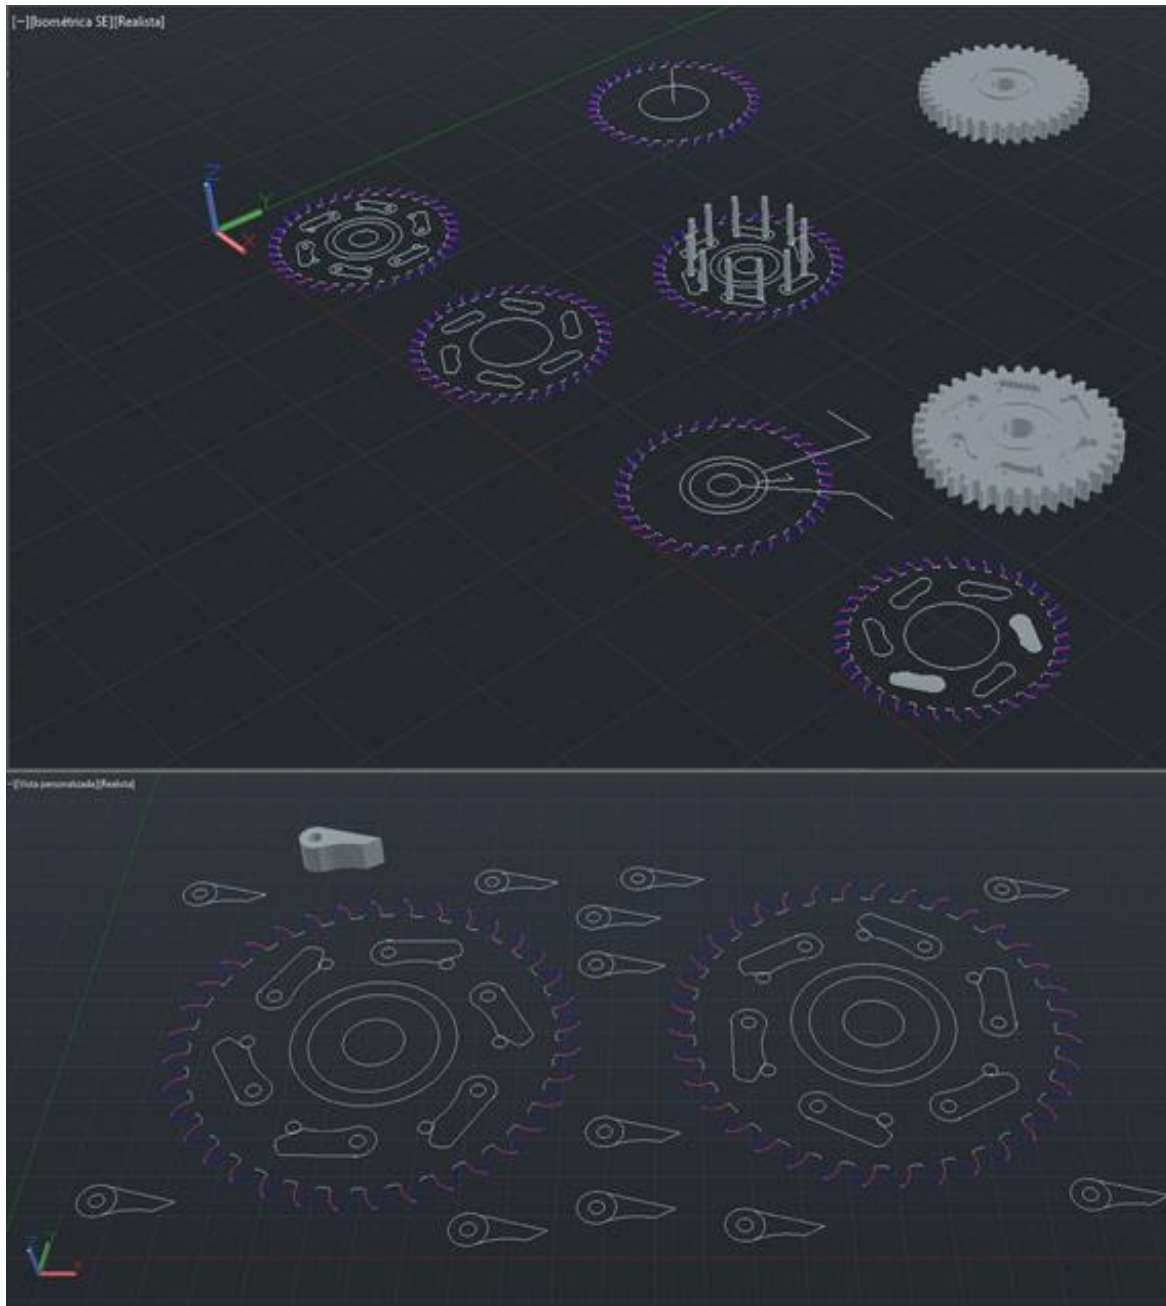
Sistema de trinquete en plano 2D y 3D AutoCAD.
